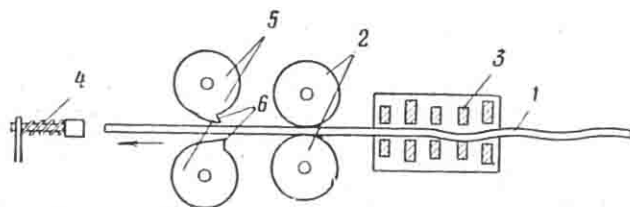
Схема работы станка АН-8 конструкции Н. Е. Носенко:
